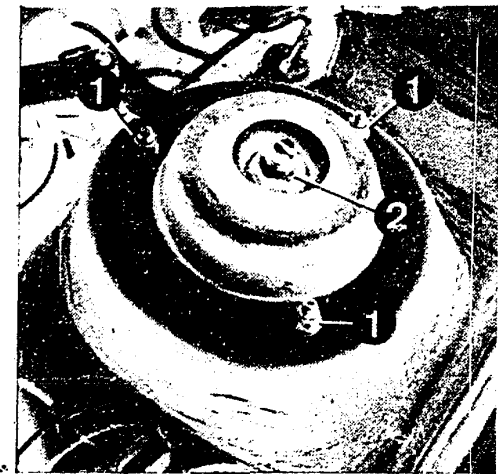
Federbeinbefestigung: 1 Befestigungsmutter – 2 Kolbenstangenmutter – 3 Drehteller – 4 Anschlaggummi – 5 Anschlag-Teller.
